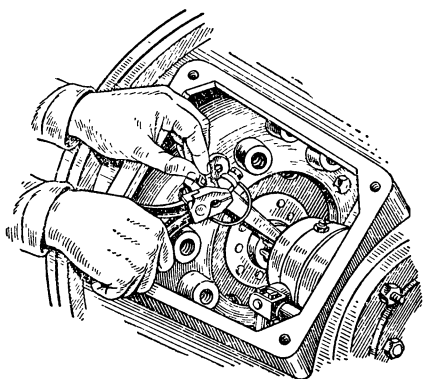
Расшплинтовывание корончатой гайки болта отжимного рычага.
